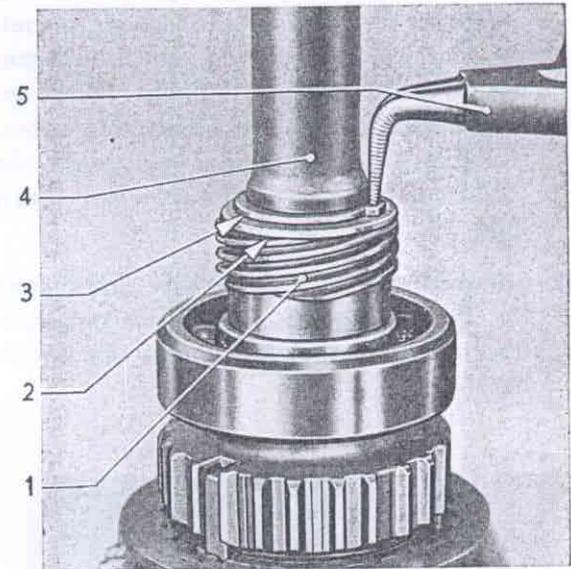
Sprengring hinter Tachometerschraubenrad aus Hauptwelle herausdrücken
